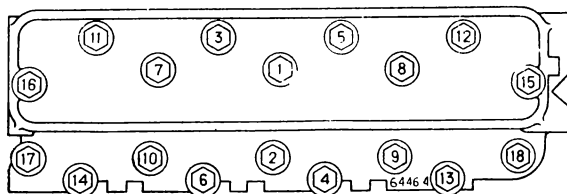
Порядок подтяжки гаек крепления головки цилиндров
